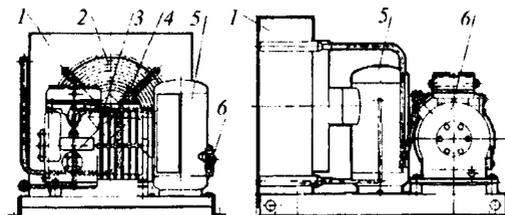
Компрессорно-конденсаторный агрегат:
